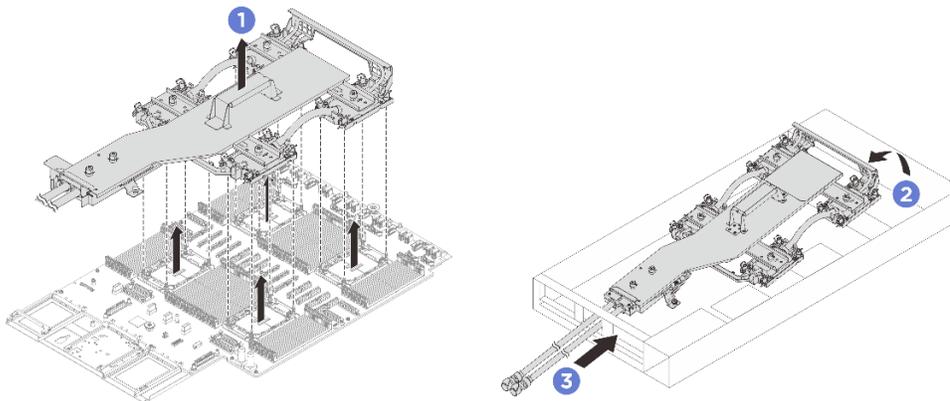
Entfernen der Kühlplattenbaugruppe
